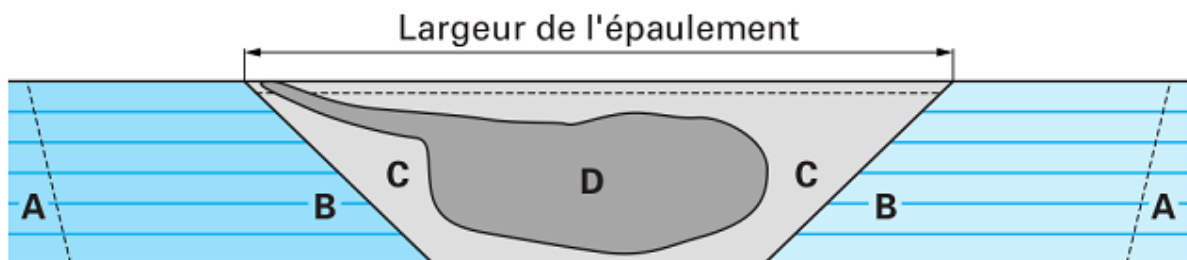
Schéma d'une coupe transversale d'une soudure FSW.
